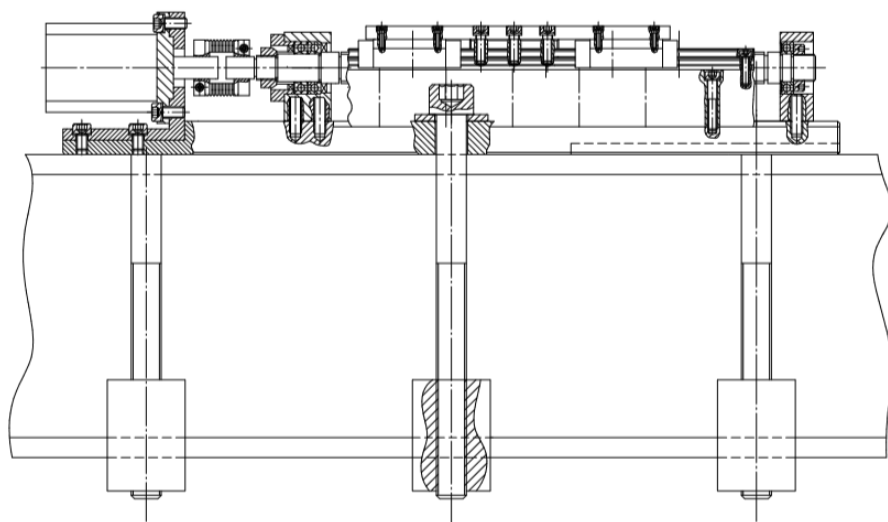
Главный вид мобильного 3-х координатного фрезерно-мобильного станка
